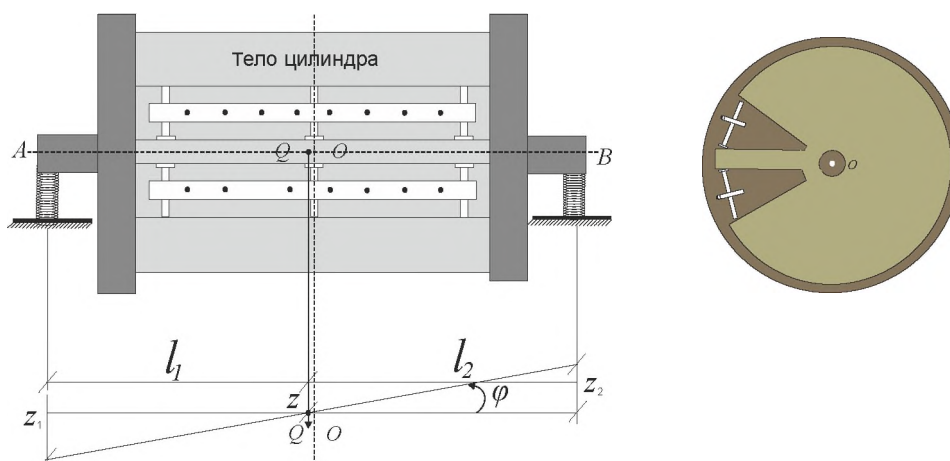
Стандартный формный цилиндр: вид спереди и с торца.
